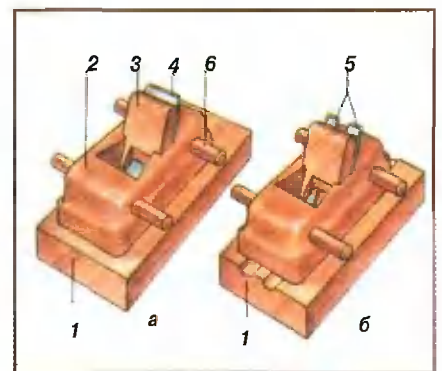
Медведки: а — для строгания больших поверхностей; б — для выстругивания желобков; 1 — обрабатываемая заготовка; 2 — колодка; 3 — клин; 4 — нож с прямым лезвием; 5 — ножи с овальным лезвием; 6 — цилиндрические ручки.
